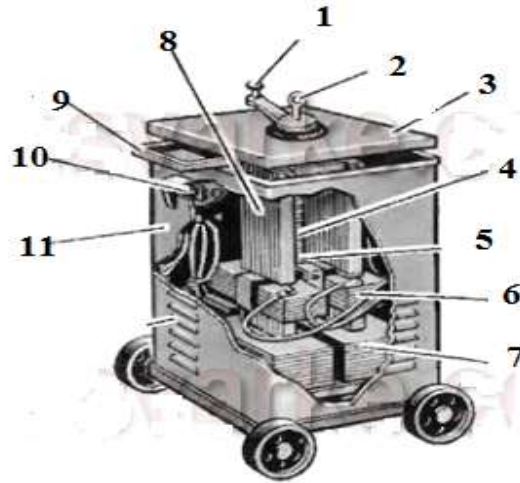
Сварочный трансформатор в разрезе.
